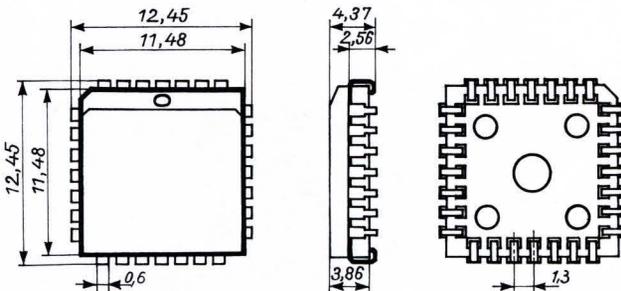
28poliger Leadless Chip Carrier (PLCC), Typkennzeichnung mit Buchstaben J
